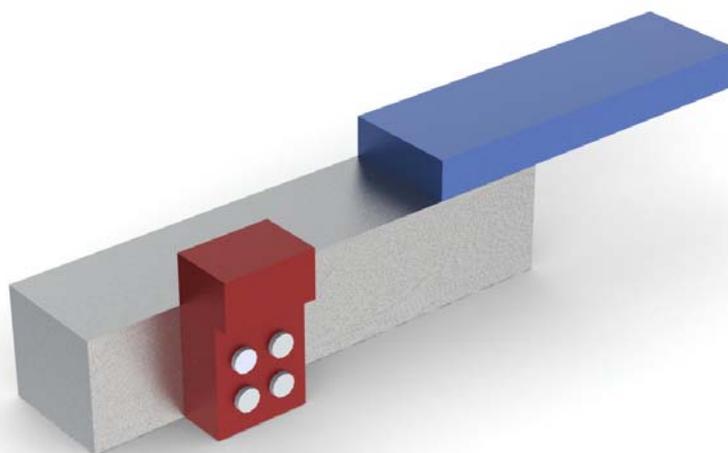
Брусок с магнитной пластиной и калибровочным эталоном толщины
